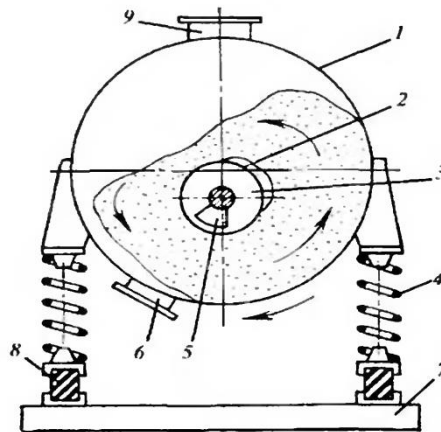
Схема вібраційного змішувача безперервної дії: 1 – корпус; 2 – труба; 3 – вал; 4 – пружина; 5 – дебаланси; 6 – розвантажувальний штуцер; 7 – станина; 8 – амортизатори; 9 – завантажувальний штуцер
